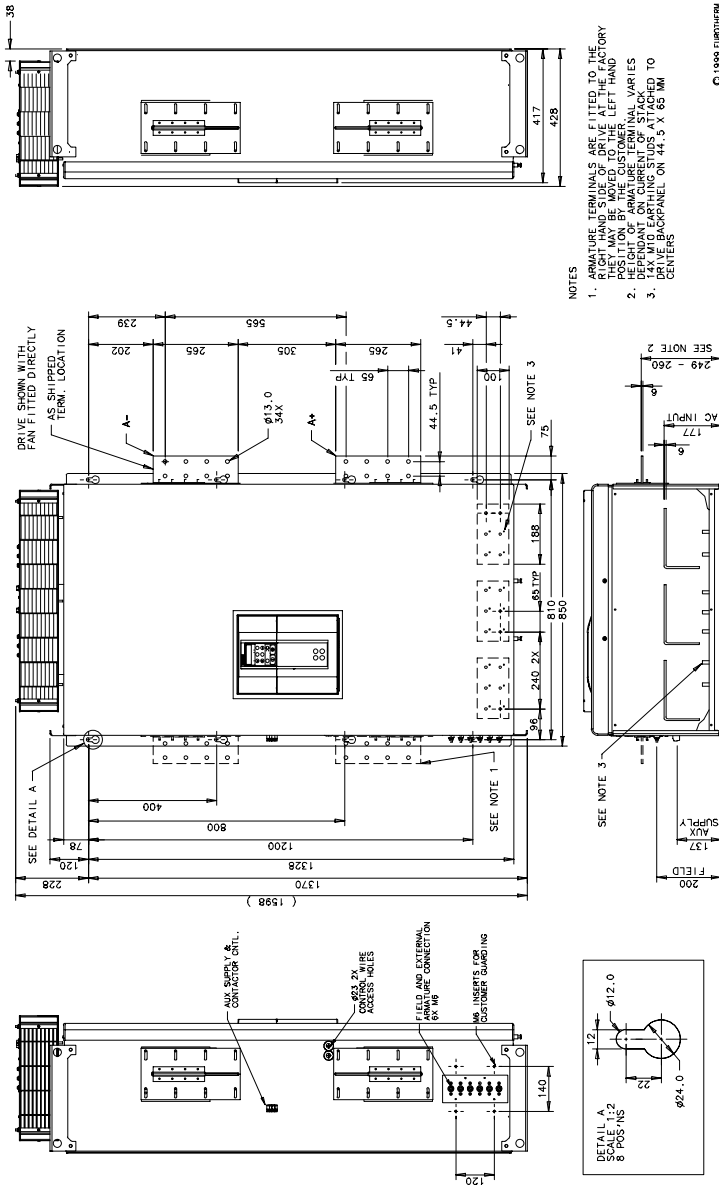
Taille 5 Ensemble de puissance 1580A (ref. HG466700U110)
